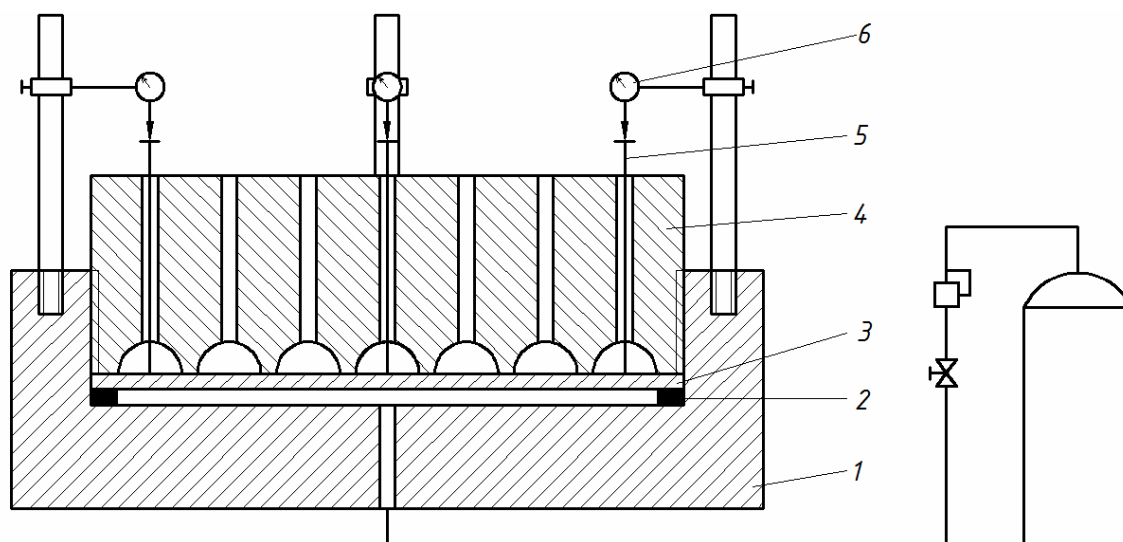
Схема устройства для штамповки: 1 – корпус; 2 – уплотнение; 3 – заготовка; 4 – матрица; 5 – толкатель; 6 – индикатор.
